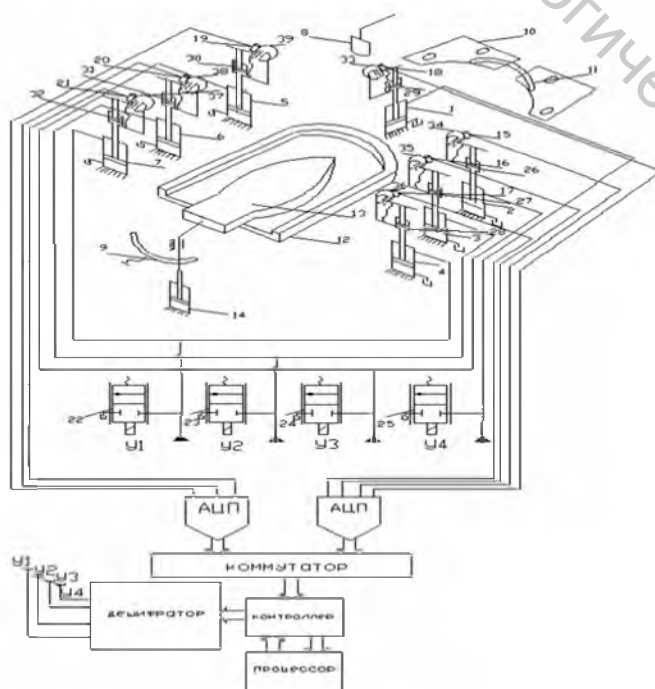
Кинематическая схема машины для затяжки верха обуви
